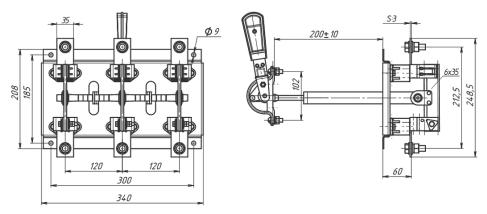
Разъединитель серии Р с центральным приводом РЦ-6 на номинальный ток 630 A
